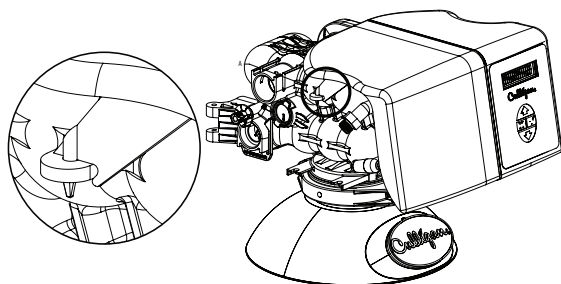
Clip de fixation du couvercle de l'adoucisseur HE
